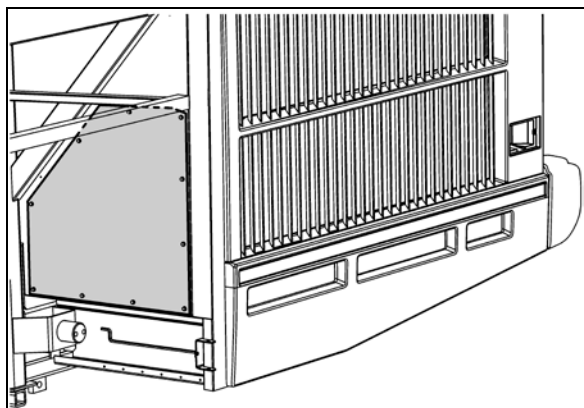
PANNEAU D'ACCÈS DERRIÈRE LA ROUE D'ESSIEU AUXILIAIRE
